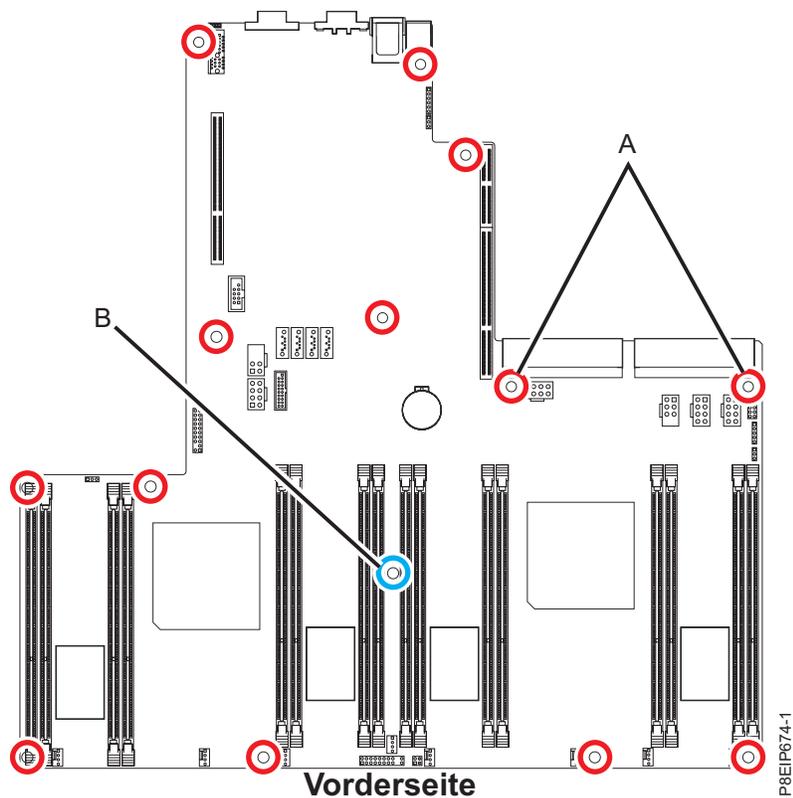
Schraubenpositionen. Die zwei Schrauben an Position (A) sind schwarz und etwas länger. Mit einer langen Schraube an Position (B) ist der PCIe-Adapter befestigt.
